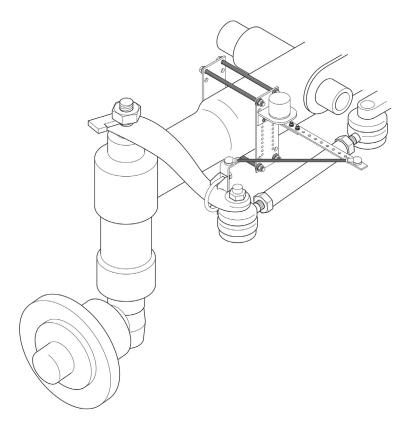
Установленное крепление датчика угла поворота на рулевую тягу в сборе
